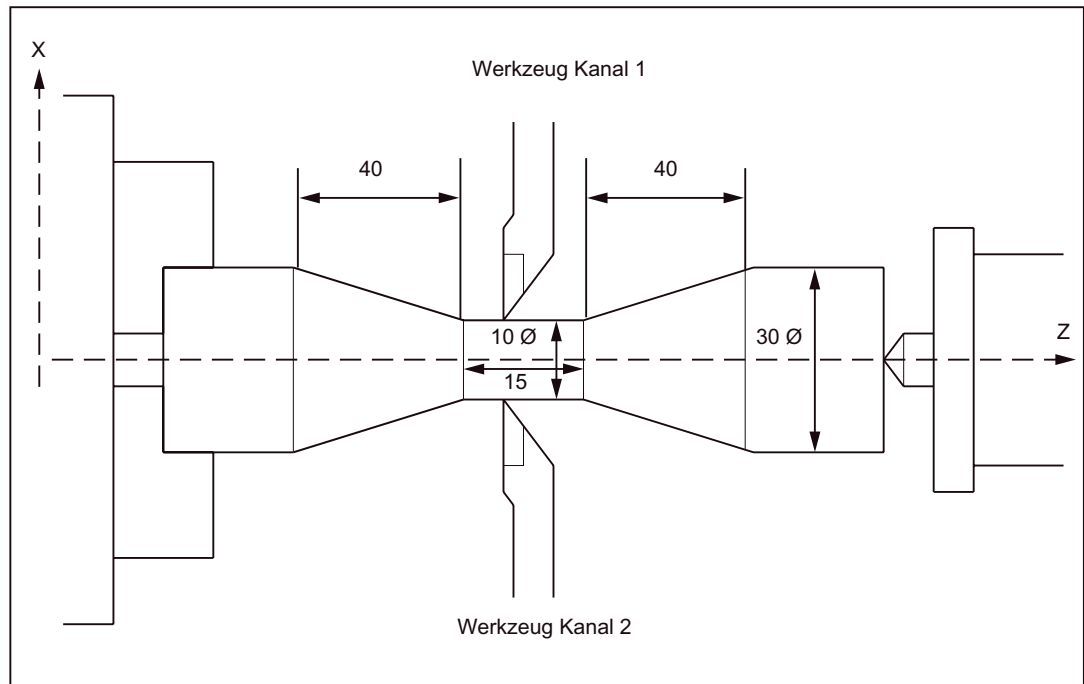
Synchrone Bearbeitung mit 2 Kanälen
